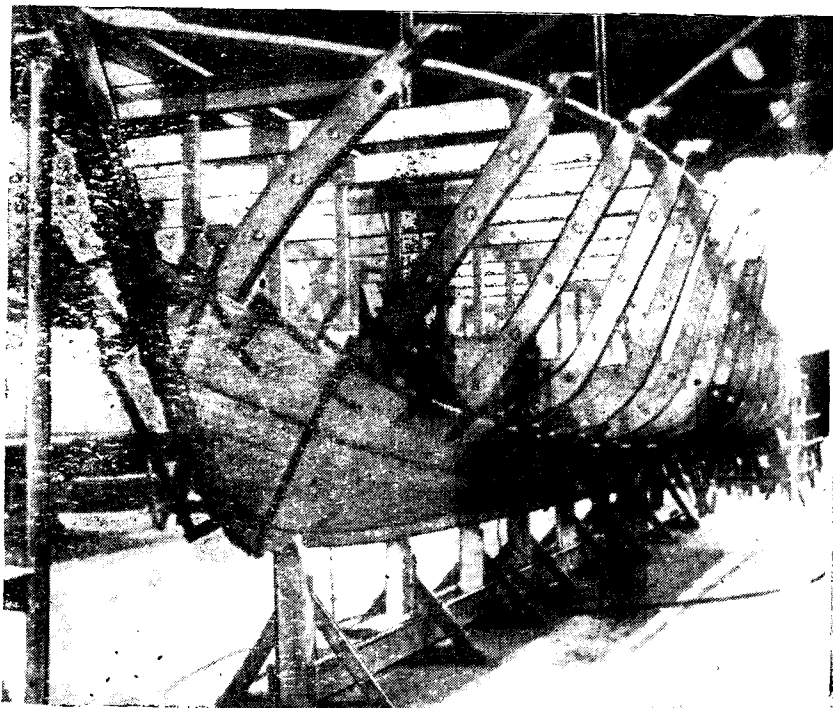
При обшивке корпуса по поперечным шаблонам отдельные планки склеивают по пазам. К килю и форштевню планки крепят на шурупах.
